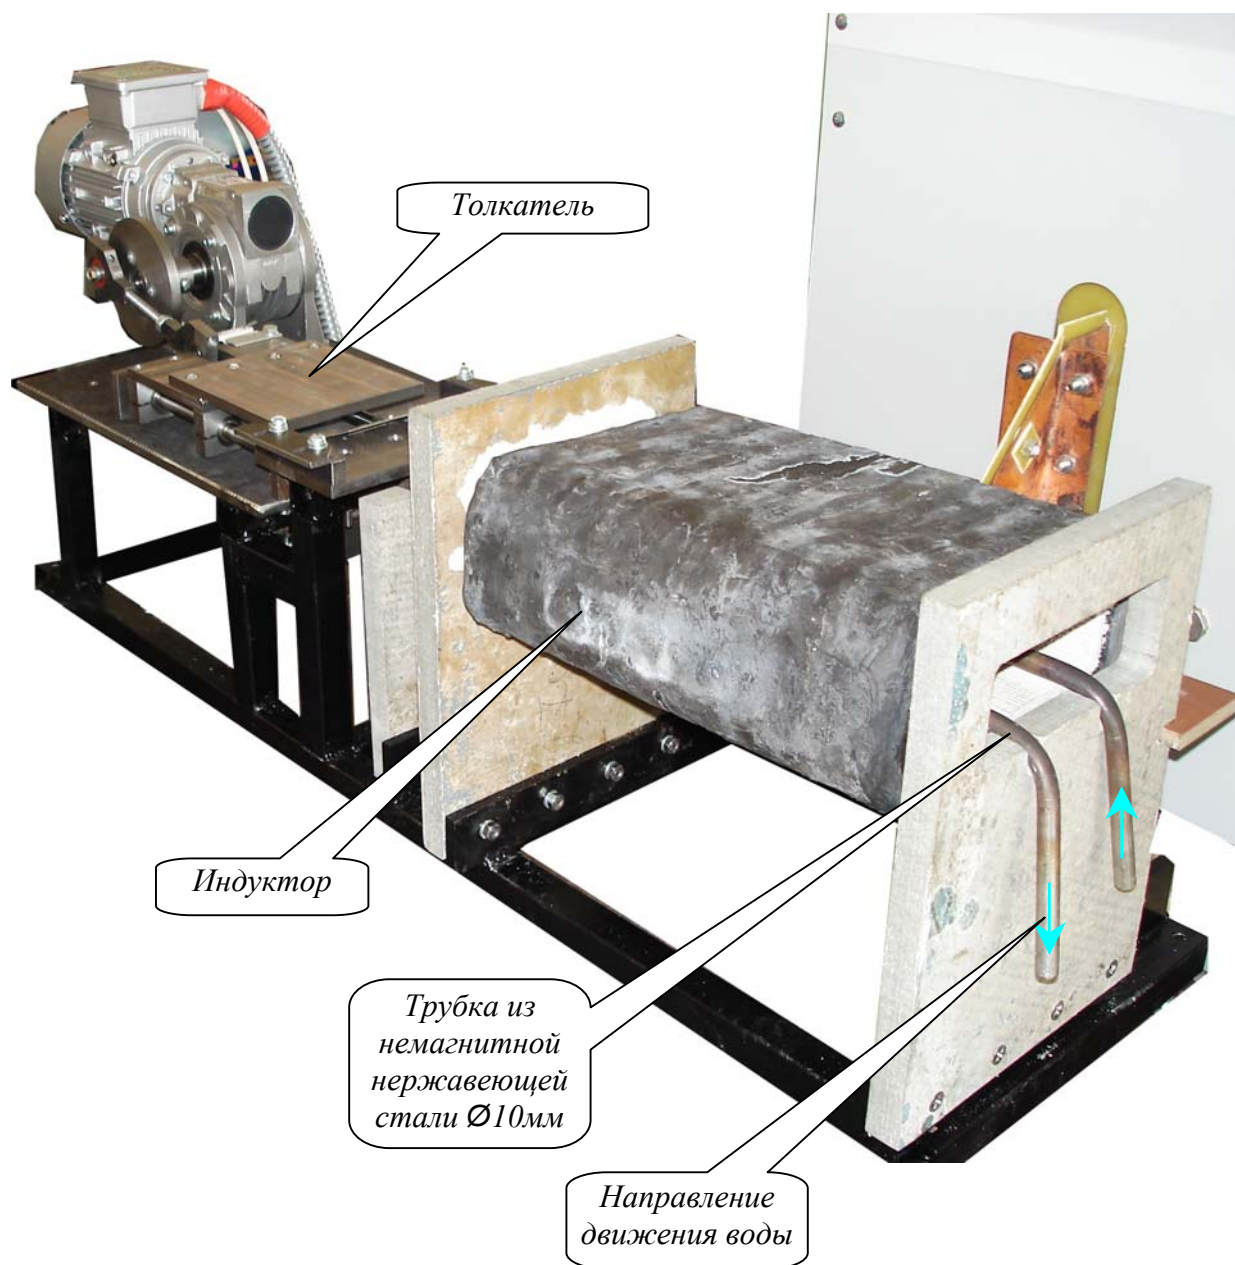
Устройство подачи заготовок в индуктор (общий вид)
